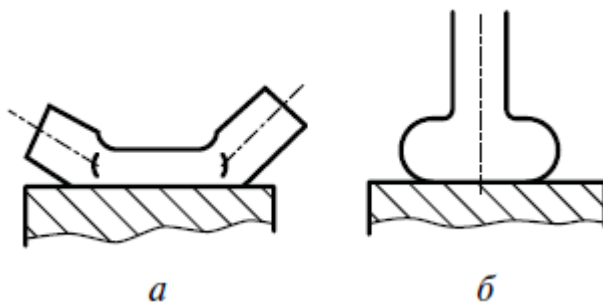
Сварные соединения: *а* – внахлест, *б* – встык с образованием шарика
